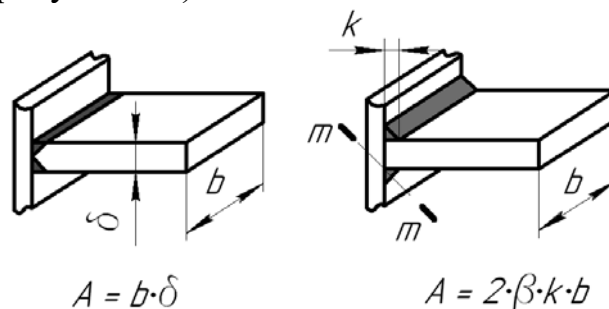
Сварное соединение полос, выполненное тавровыми сварными швами
